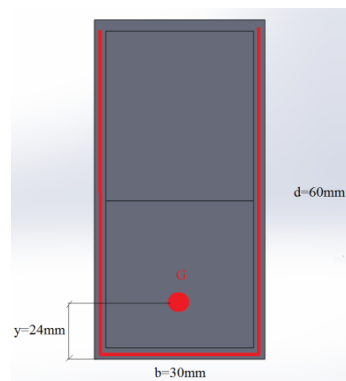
Soldadura entre els diferents mòduls del transportador.
